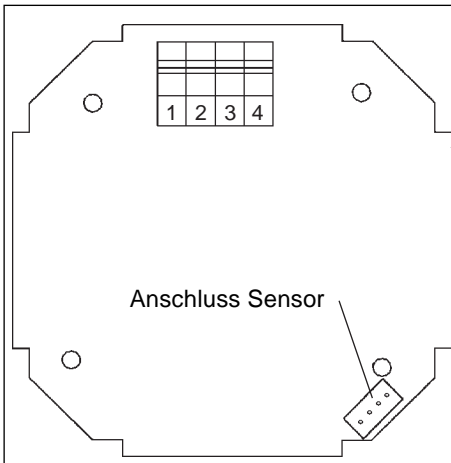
Anschlussbelegung 8225 mit Kabelverschraubung
